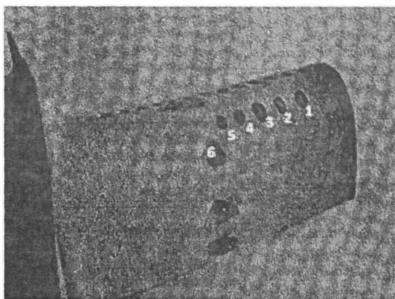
Внешний вид зон (1-5) лазерной абляции лопатки турбины реактивного двигателя
